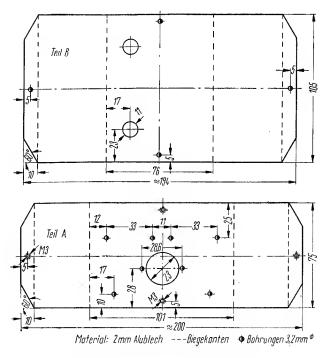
Maßskizze für das Chassis des KW-Kanverters
